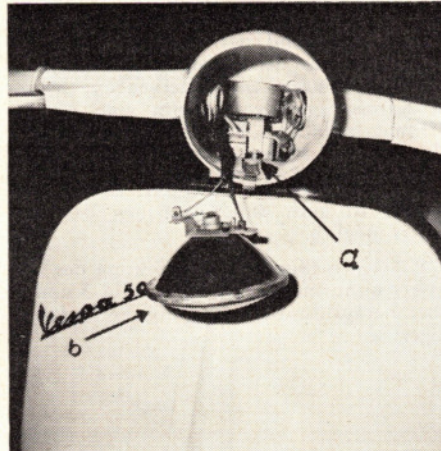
a = Klemmschraube für Tachobefestigung, b = Scheinwerferanschlüsse.
